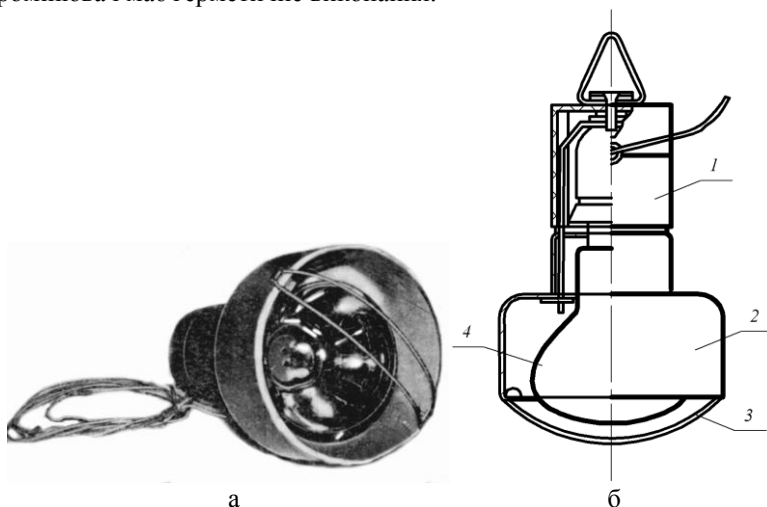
Опромінювач ветеринарний типу ОВИ-1: а) загальний вигляд; б) розріз: 1 – корпус; 2 – пластмасовий ковпак; 3 – захисна сітка; 4 – ІЧ-лампа
